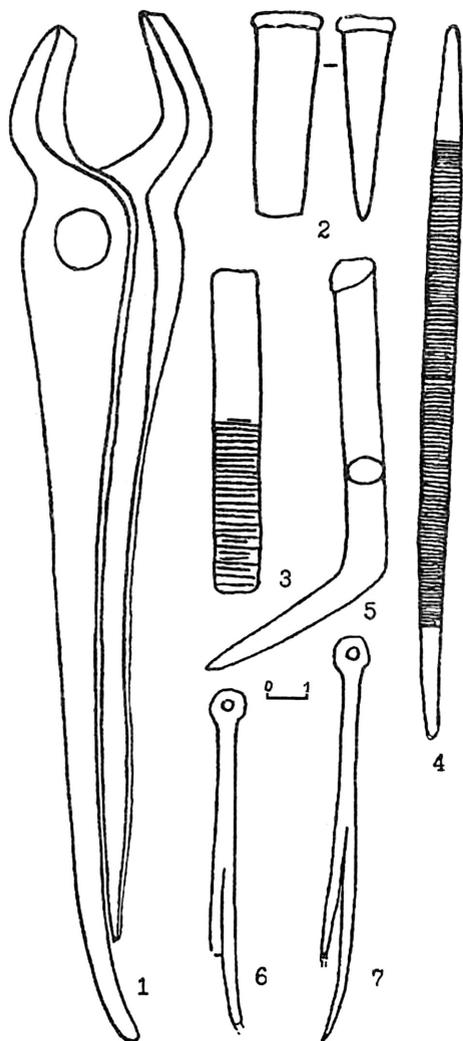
Кузнечно-слесарный инструментарий: 1 — кричные клещи; 2 — зубильце; 3, 4 — напильники; 5 — пробойник; 6, 7 — пинцеты
